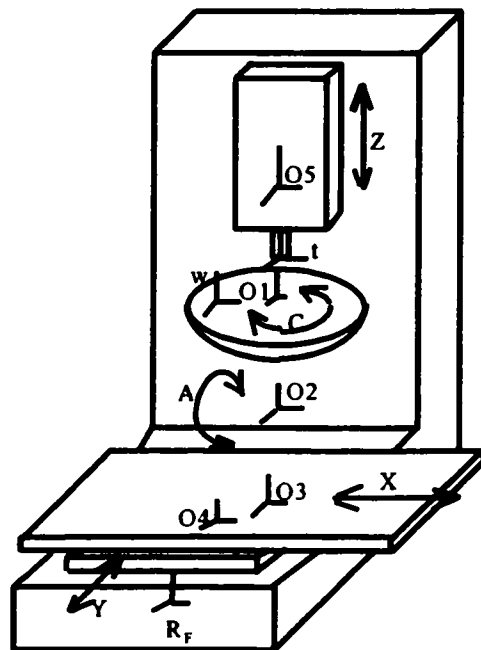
Centre d'usinage à 5 axes Matsuura
